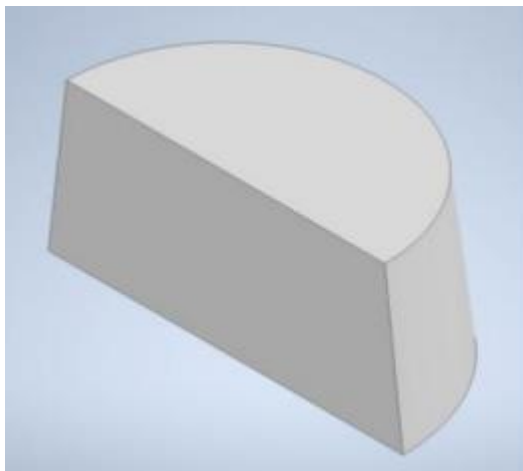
3D-модель деталі "Платформа камери"
